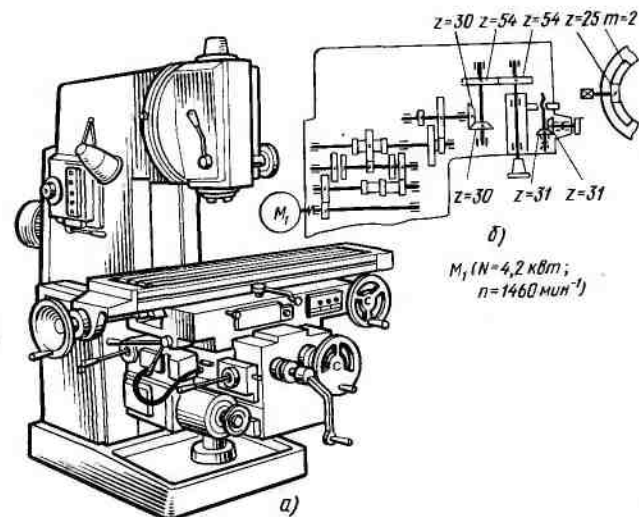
Консольный вертикально-фрезерный станок мод. 6P12 (а) и кинематическая схема поворотной шпиндельной головки (б)
